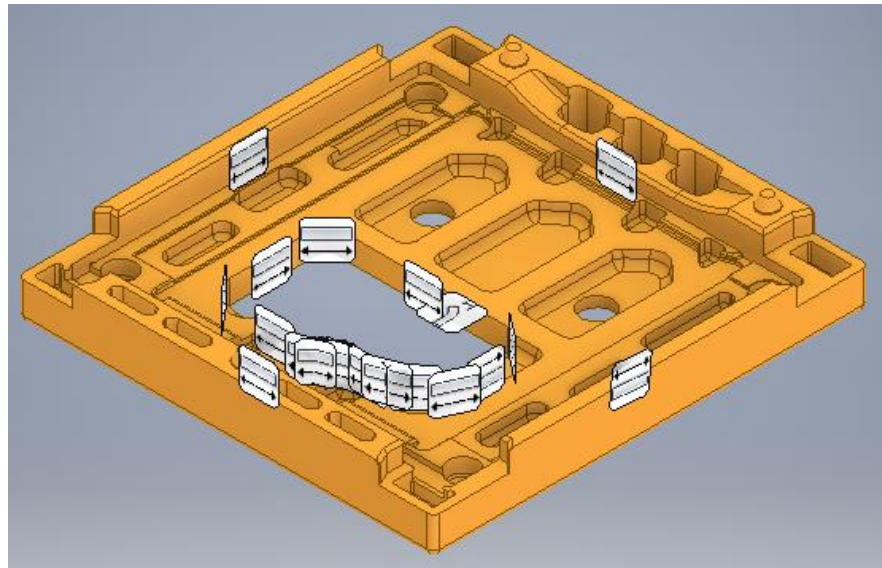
Restricciones de movimiento en el embalaje de lavadora con fondo
